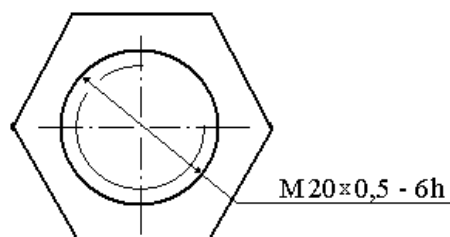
Обозначение наружной резьбы на чертеже (вид справа)
